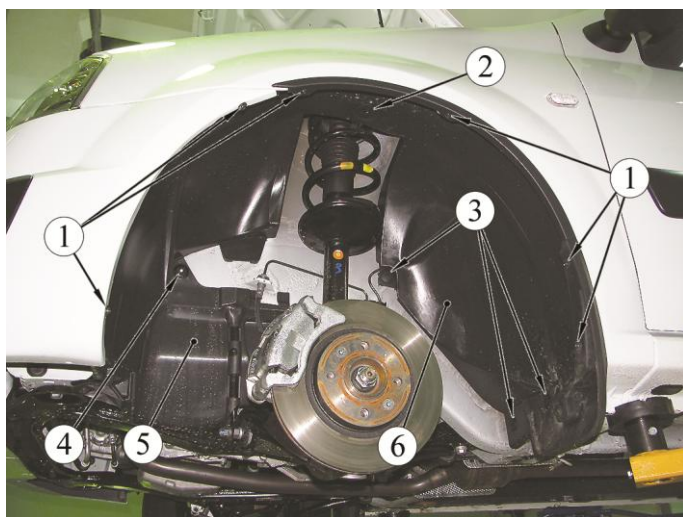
Кожух защитный арки переднего колеса:
